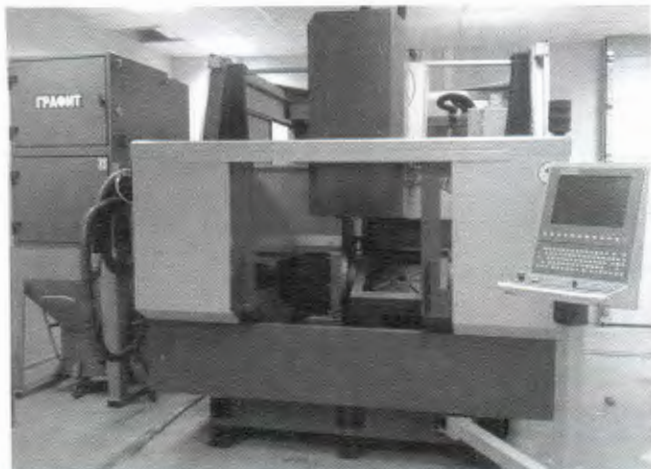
Опытный образец обрабатывающего центра по обработке графитовых электродов, оснащенный комплектной системой ЧПУ СТАНКИН NC 201
